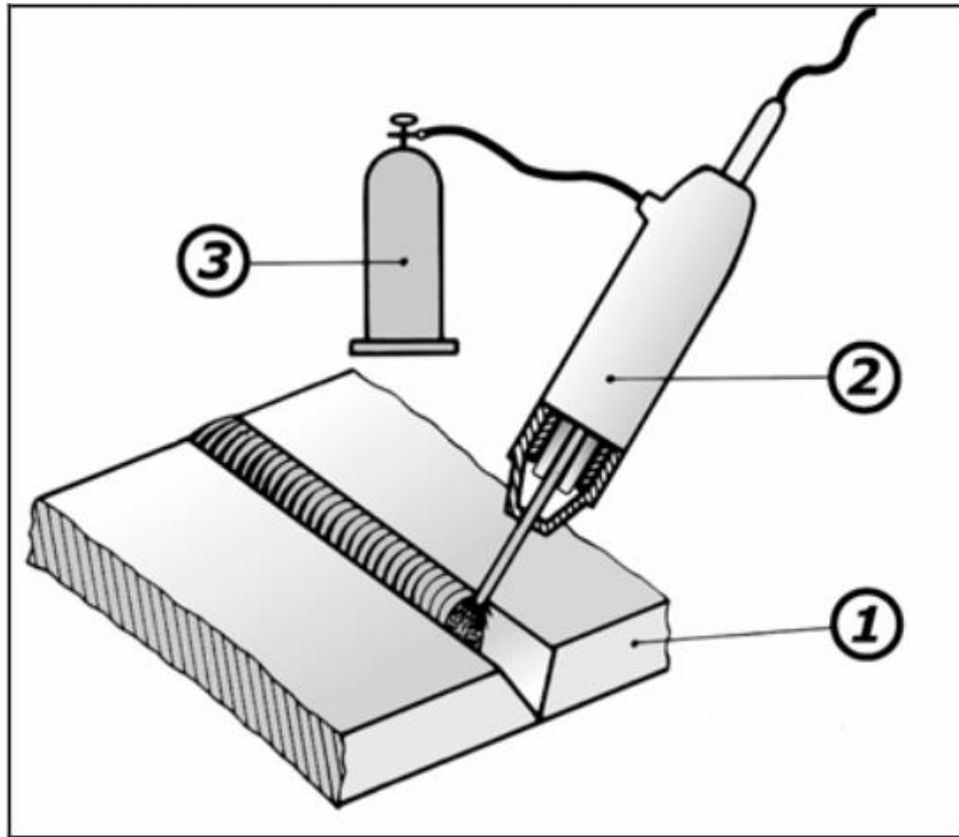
Soldadura en una atmósfera de gas protector [18].
